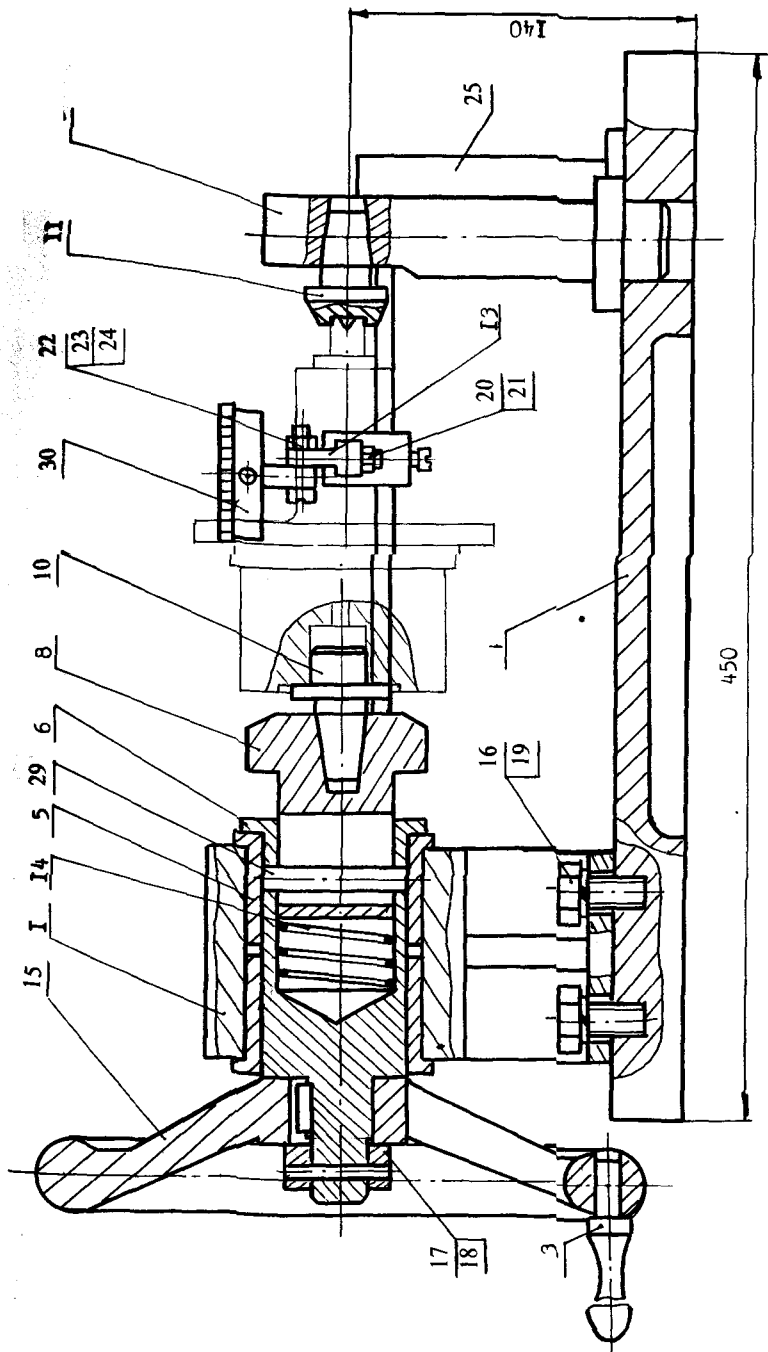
Приспособление для контроля радиального и торцового биений:
